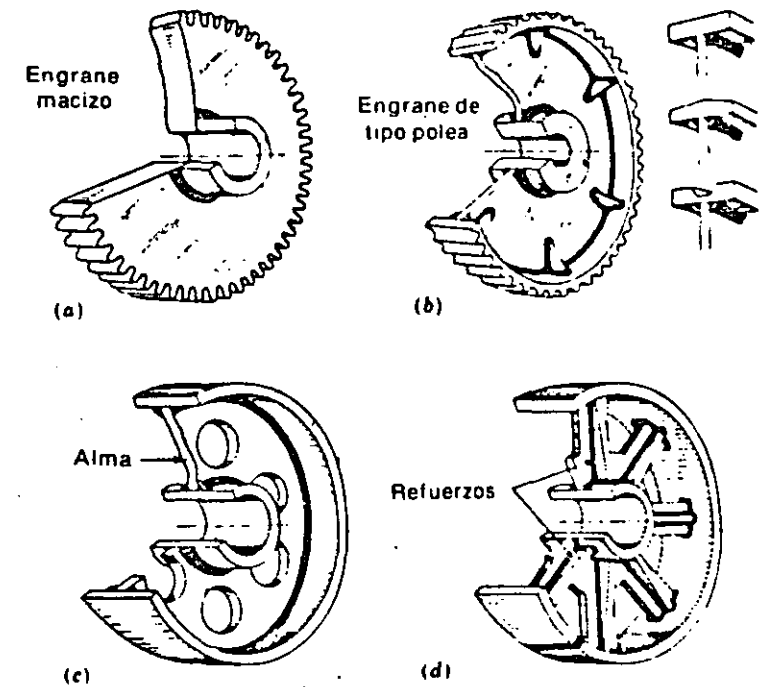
Tipos de fabricación de engranes por soldadura: a) Cuerpo de engrane macizo con cubo soldado; b) Engrane con alma maciza y refuerzos soldados para rigidizar más el aro; c) Construcción satisfactoria para engranes de diámetro no muy grande y con ancho de cara pequeño; d) Cuerpo de engrane armado con brazos o rayos. (Cortesía de Lincoln Electric Company.)
